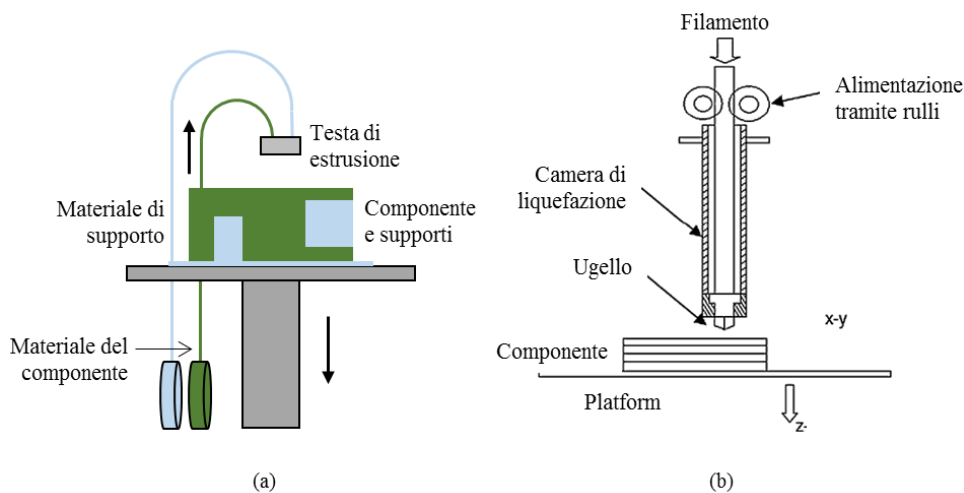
Principio di funzionamento di una macchina FDM (a) e ingrandimento della testa di estrusione (b).
